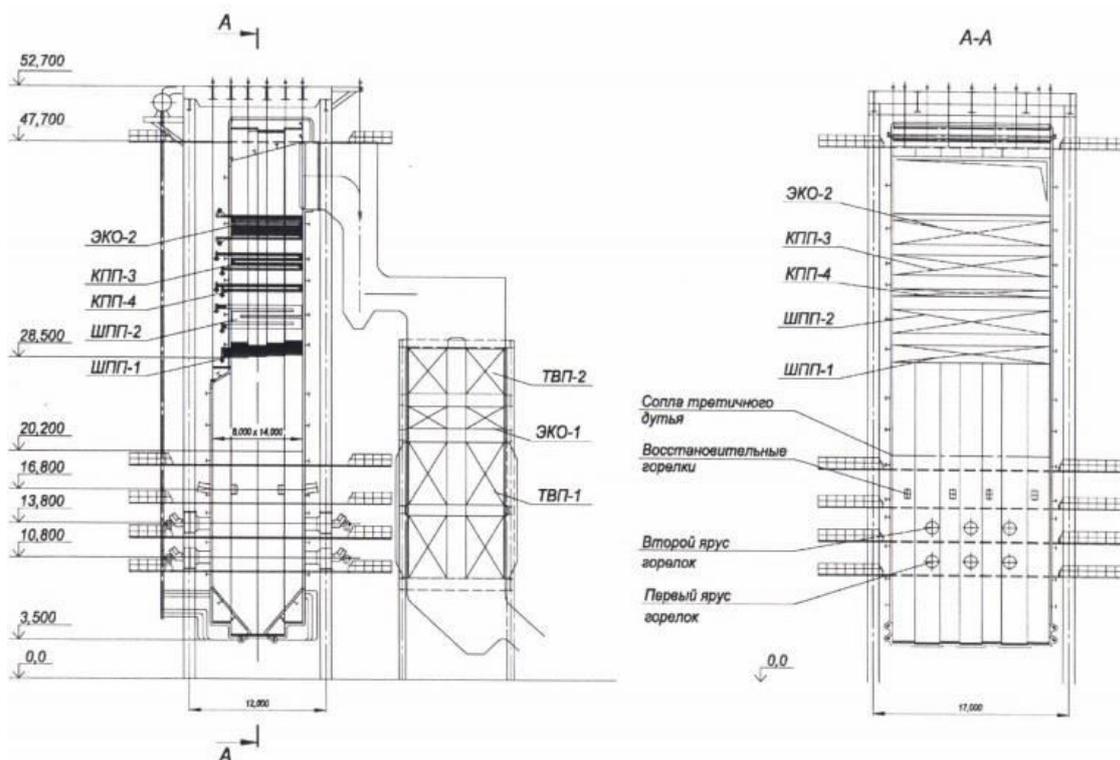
Компоновка бешенного котлоагрегата ст. №№7,8 БКЗ-550-13,8-560КТ, с расположением поверхностей нагрева
